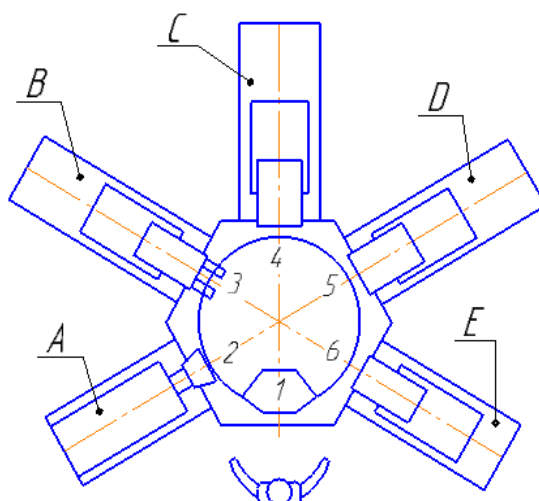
Агрегатный станок с поворотным столом “Cross”
